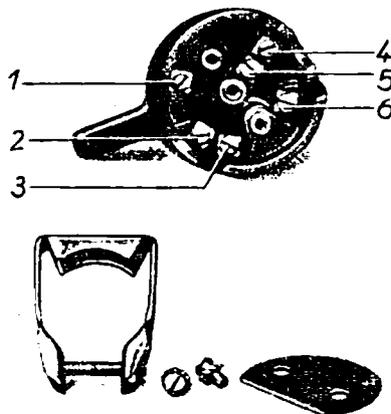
Anschlüsse des Abblendschalters RT 3 PS
